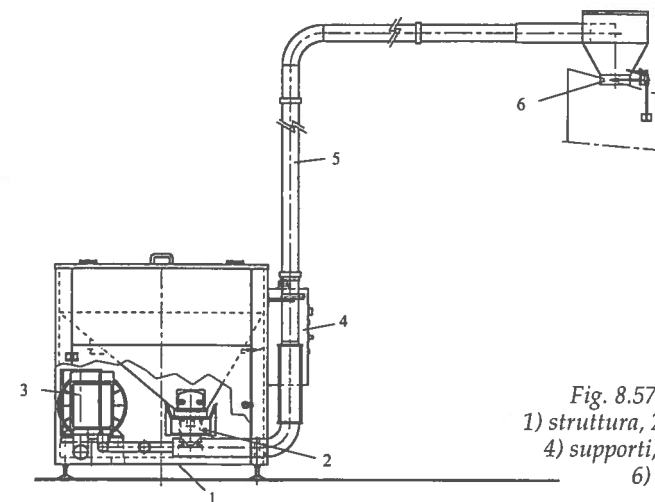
Elevatori pneumatici. 1) struttura, 2) trasportatore, 3) vibratore, 4) supporti, 5) trasportatore elevatore, 6) pressurizzazione.
